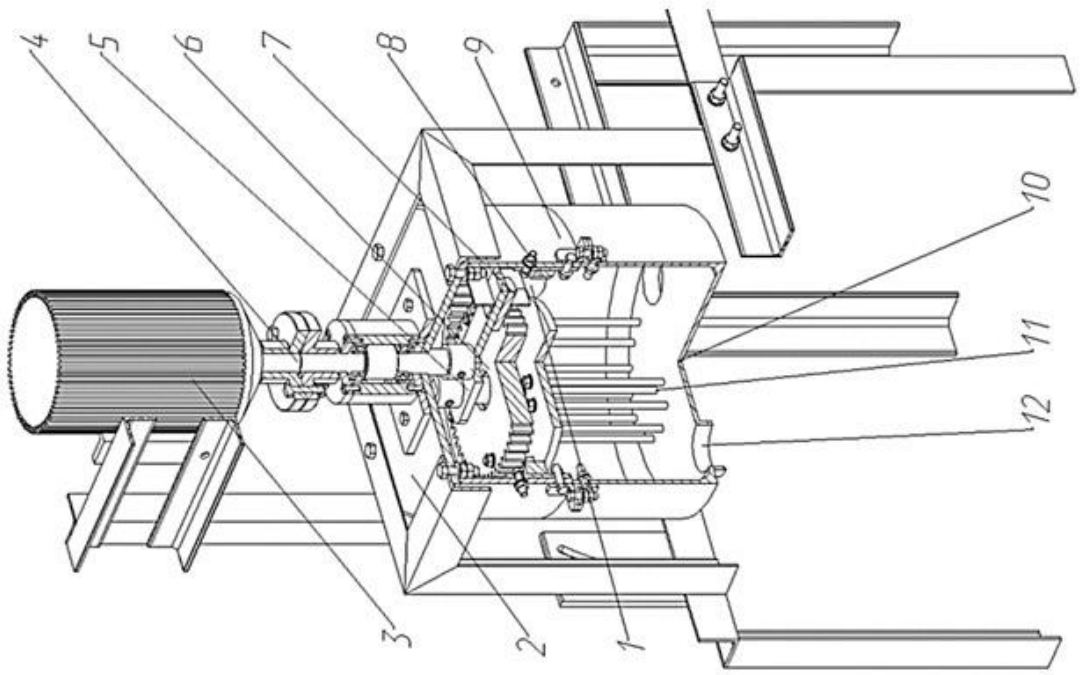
Конструкція нового планетарного змішувача сипких кормів: 1 - завантажувальний пристрій; 2 - кришка корпусу; 3-двигун; 4 - вихідний вал; 5 - повідець; 6 - шестерня; 7 - противага; 8 - зубчастий вінець; 9 - корпус; 10 - ємність; 11 - мішалка; 12 - розвантажувальний пристрій
